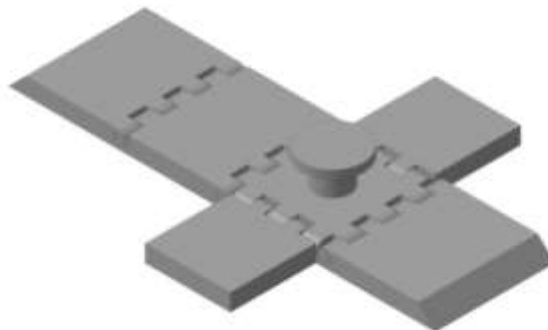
Развертка коробочки из практического задания для 10-11 классов.
